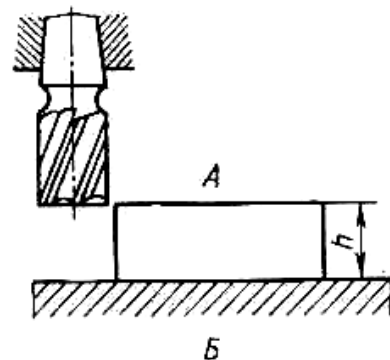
Схема базування призматичної деталі при фрезеруванні площини
